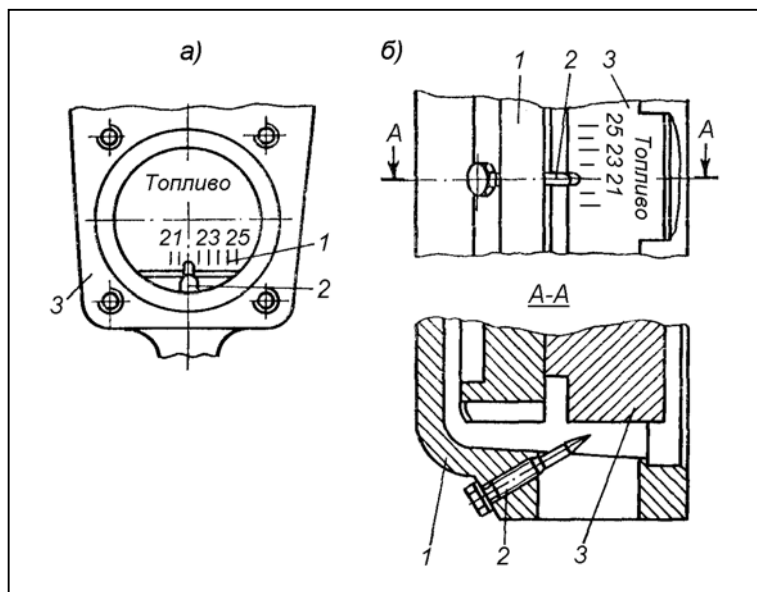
К установке положения коленчатого вала при соединении муфты привода ТНВД двигателя ЯМЗ-240БМ:
